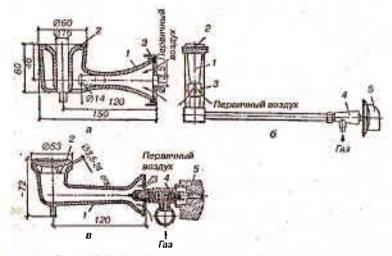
Конфорочные горелки бытовых плит: а — с центральным каналом; б — вертикальная; в — для плит П5-4 (старая); 1 — корпус горелки; 2 — рассекатель (головка); 3 — регулятор воздуха; 4 — кран; 5 — ручка крана
